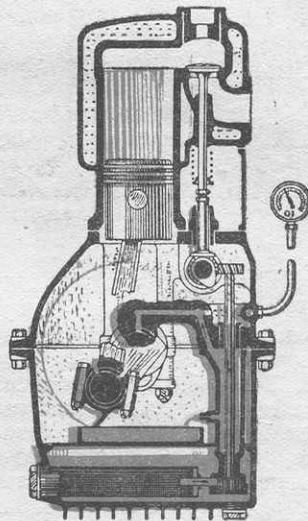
Комбинированная смазка разбрызгиванием и под давлением.
